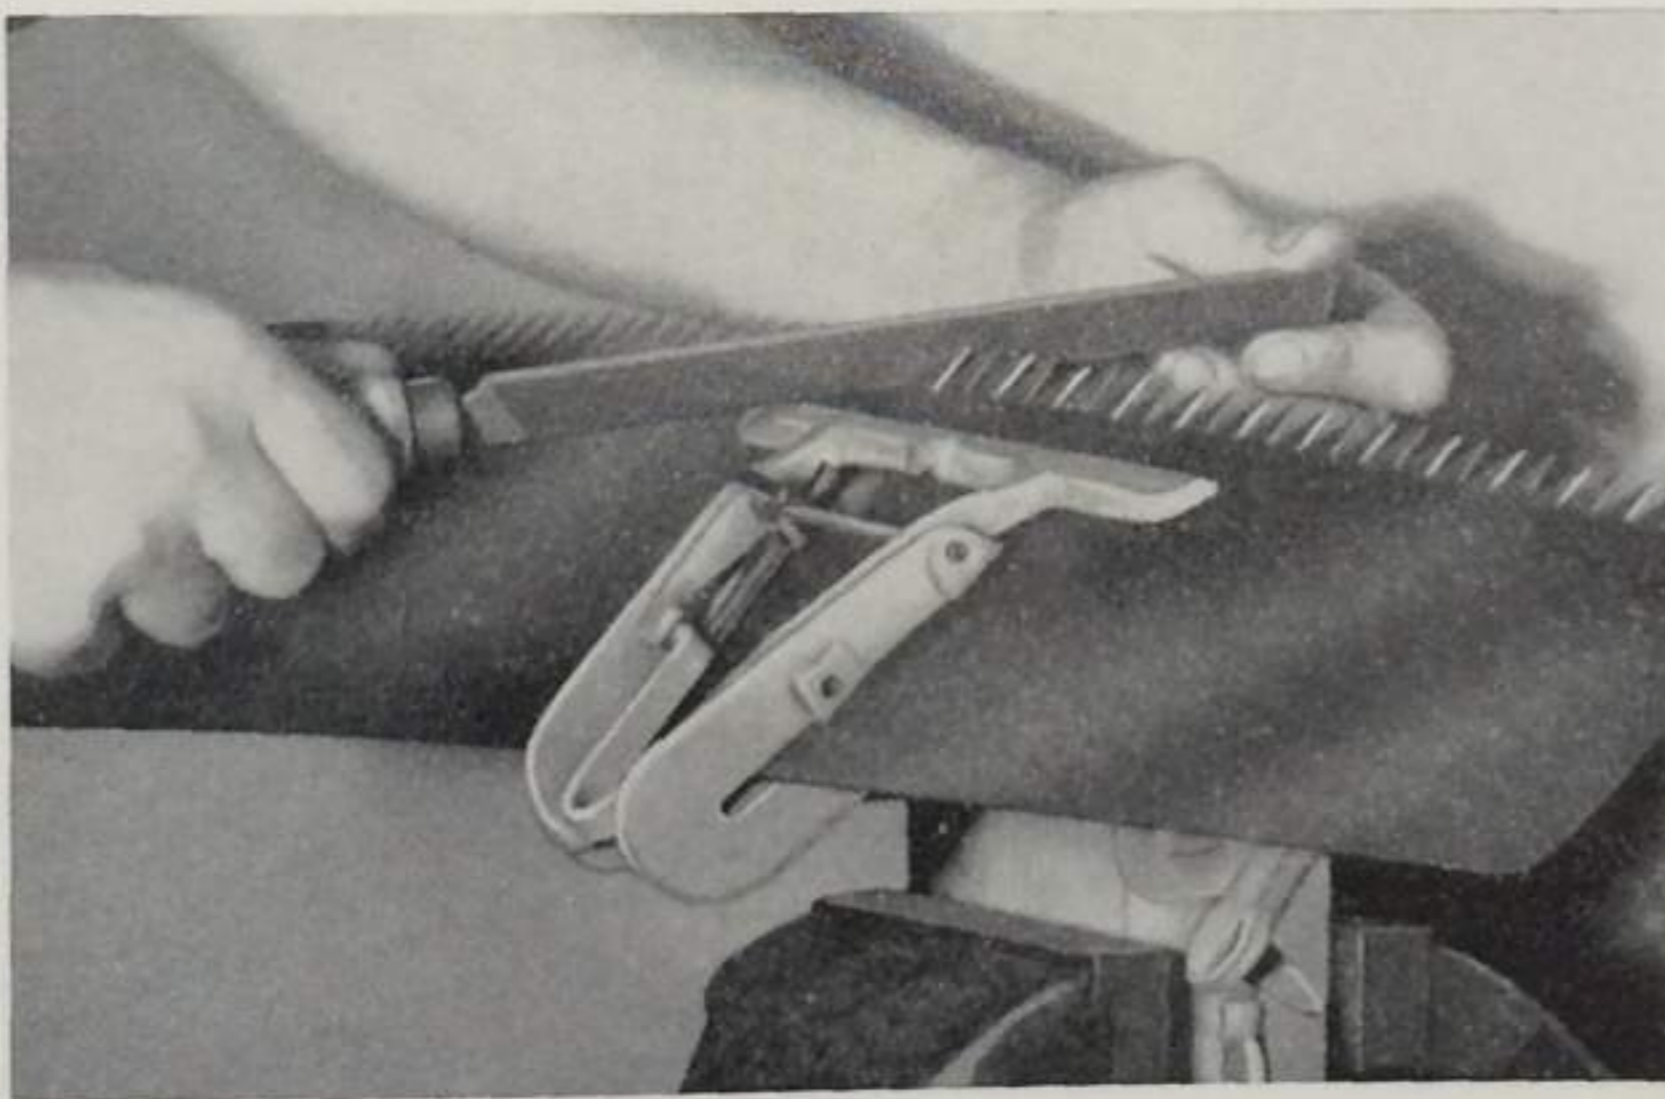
Rätt inspänt blad. Rätt lutning på filen. I ovanstående illustrationer är sågarna inspända i »Orsia» filklovar.
